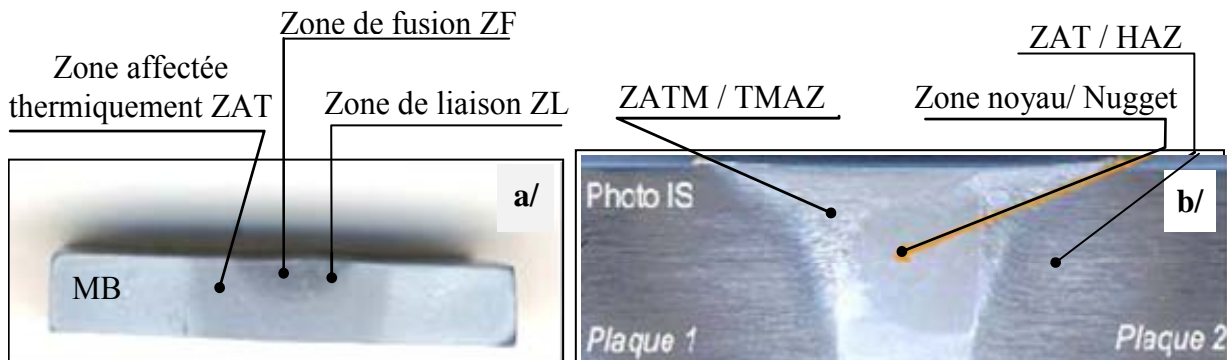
Cordons de soudure : a/ soudage à l'arc, b/ soudage par friction (FSW).
